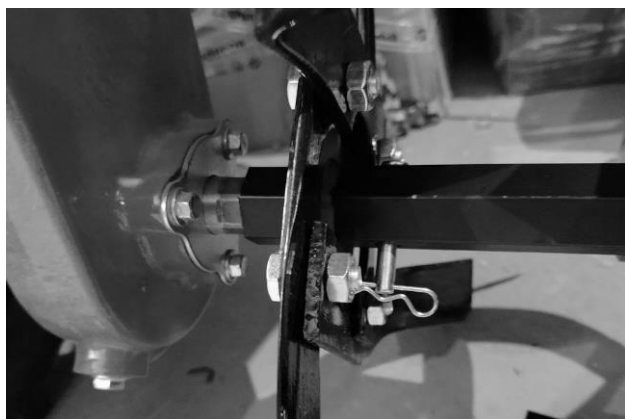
Установка фрезы в сборе на выходной вал редуктора
